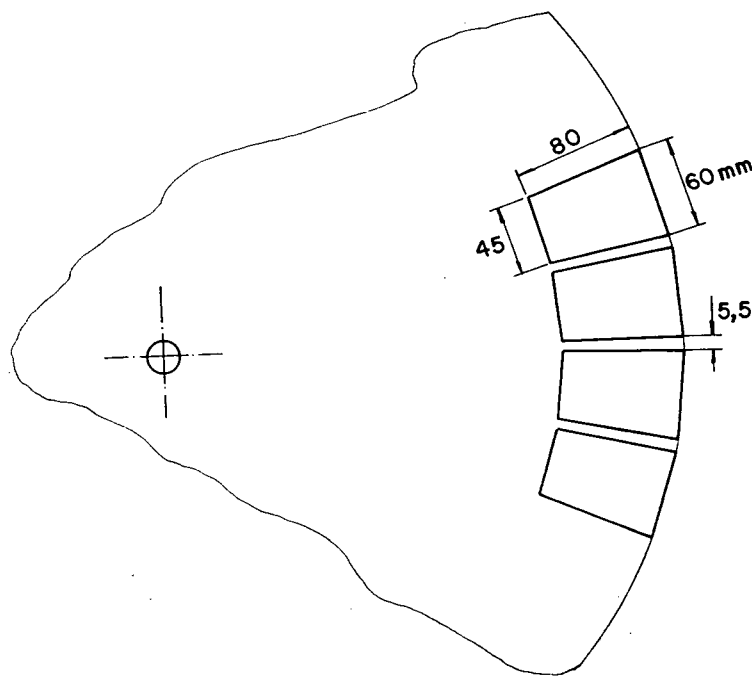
Detalhe do disco plantador mostrando as dimensões das plaquetas.
